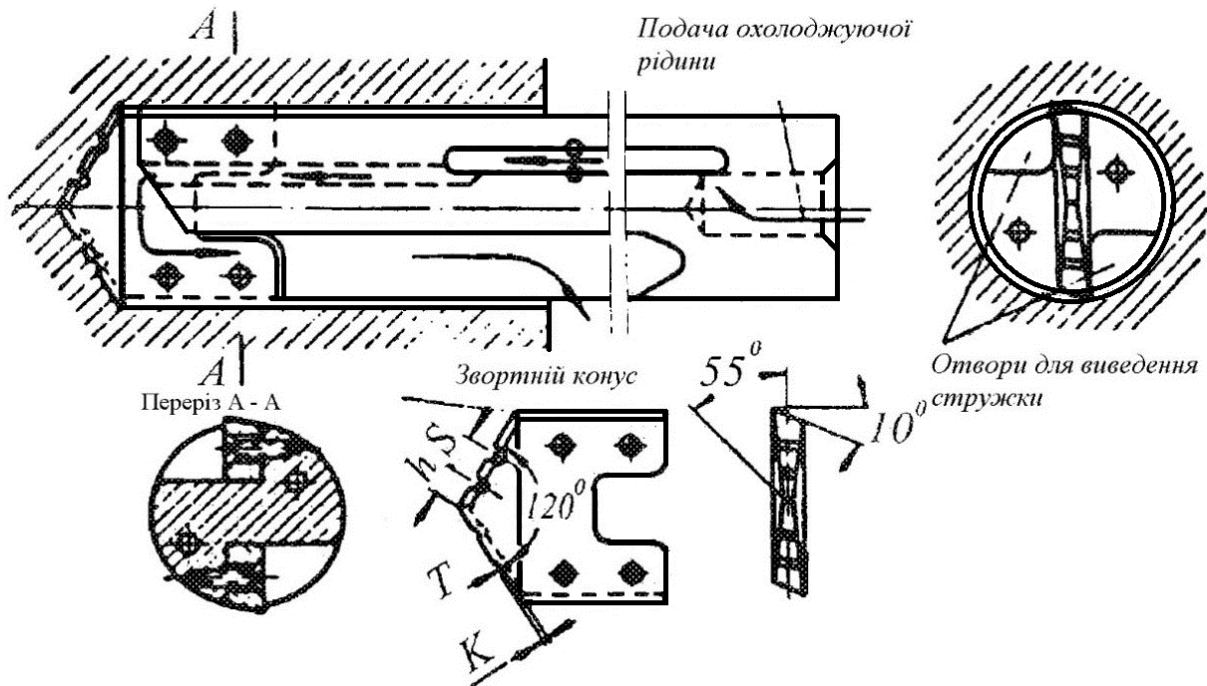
Свердло двокромочне для глибокого свердління з поліпшеними умовами центрування
